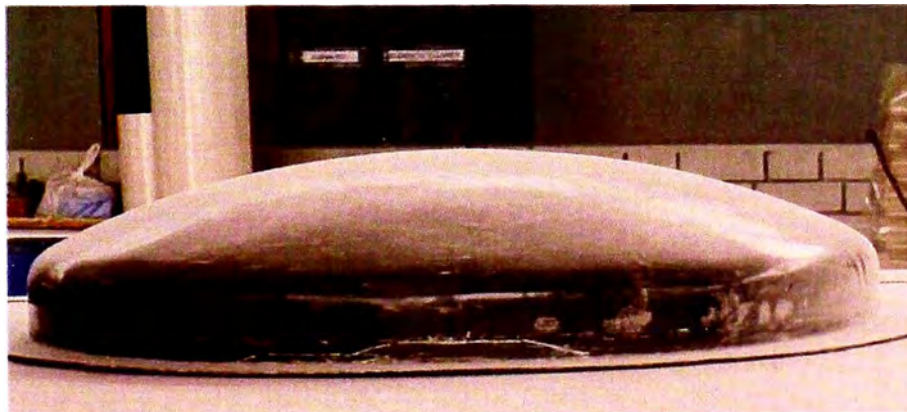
MOLDE DE FRP DE TAPAS TORIESFÉRICA.
